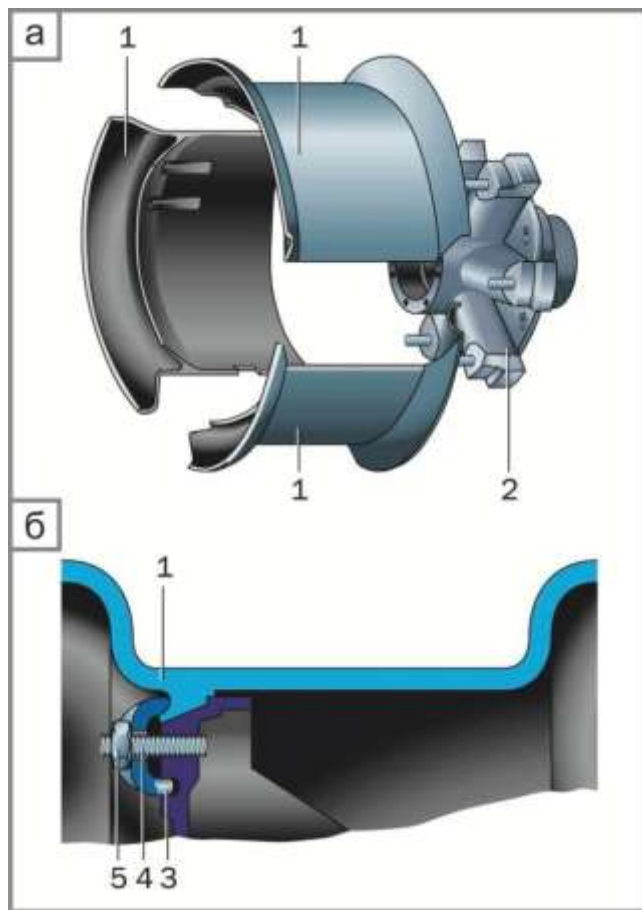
Бездискове колесо, його загальний вигляд (а) і кріплення колеса (б): 1 – сектори колеса; 2 – маточина; 3 – кріплення; 4 – шпилька; 5 – гайка
